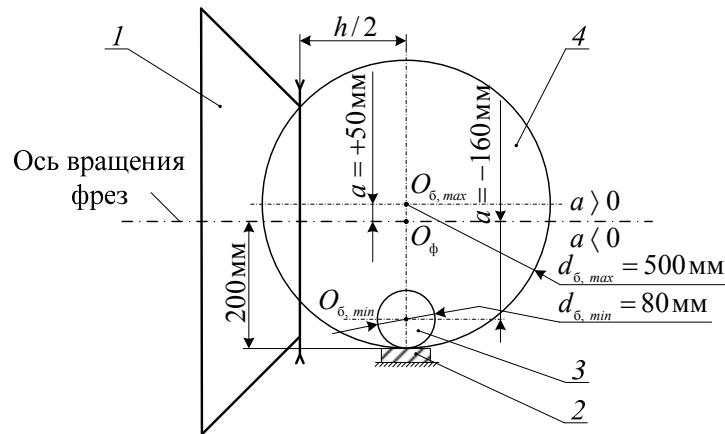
Схема обработки бревен на фрезерно-брусующем станке:
